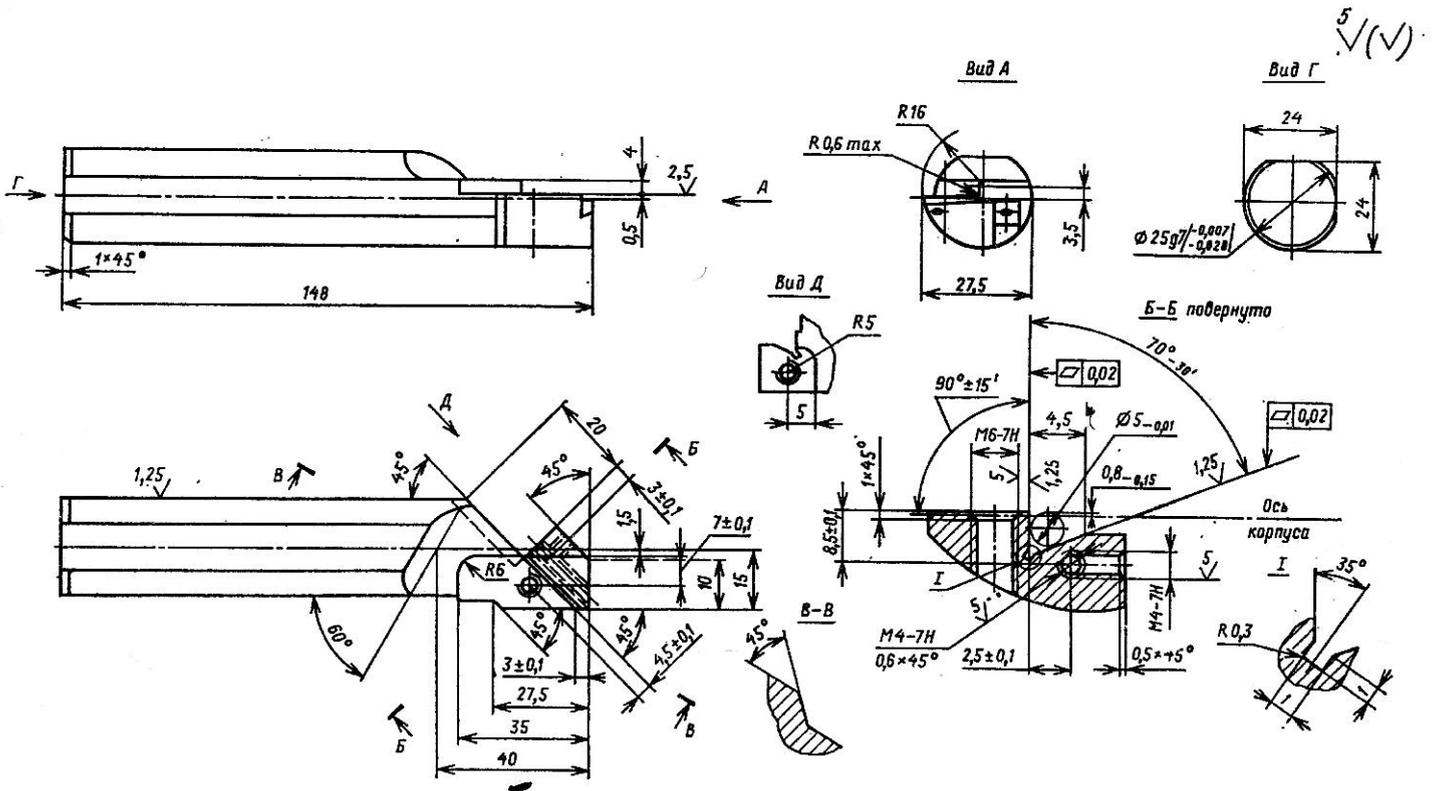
Резец для проточки внутренних угловых канавок, короткий П86-04Л-000:
